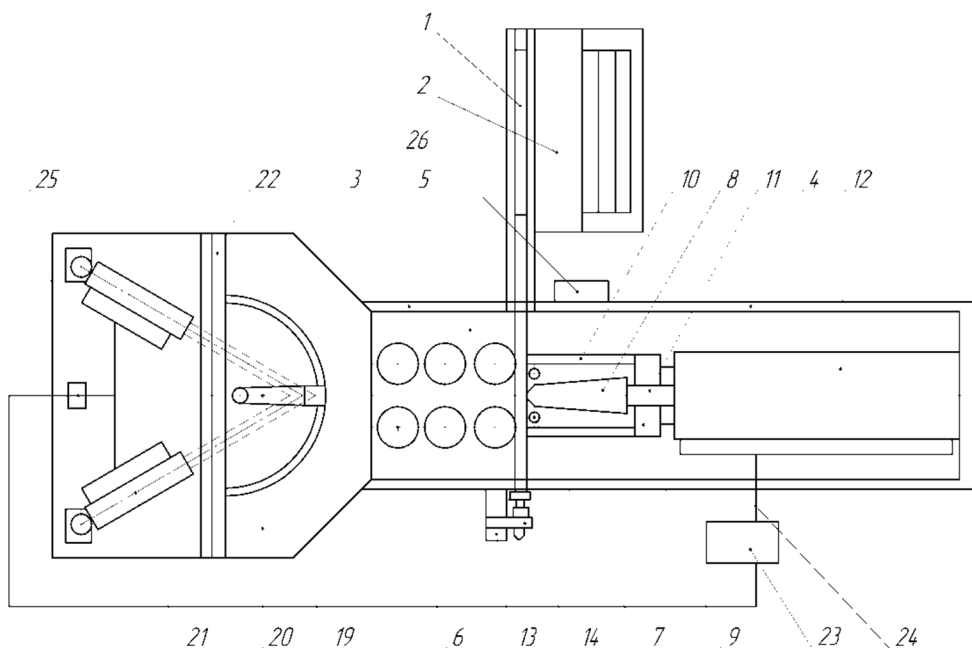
Принципиальная схема стана для прокатки заготовок малолистовых рессор автомобилей МАЗ (вид сверху)
